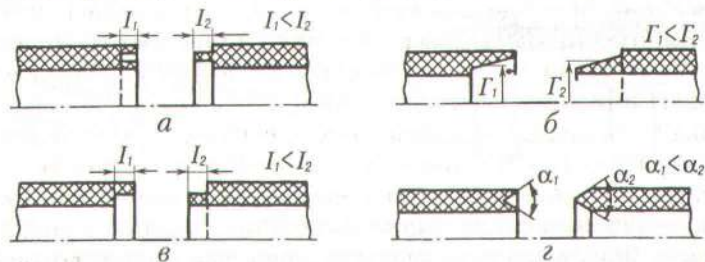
Конструкції розробки кромок труб під зварювання тертям:
